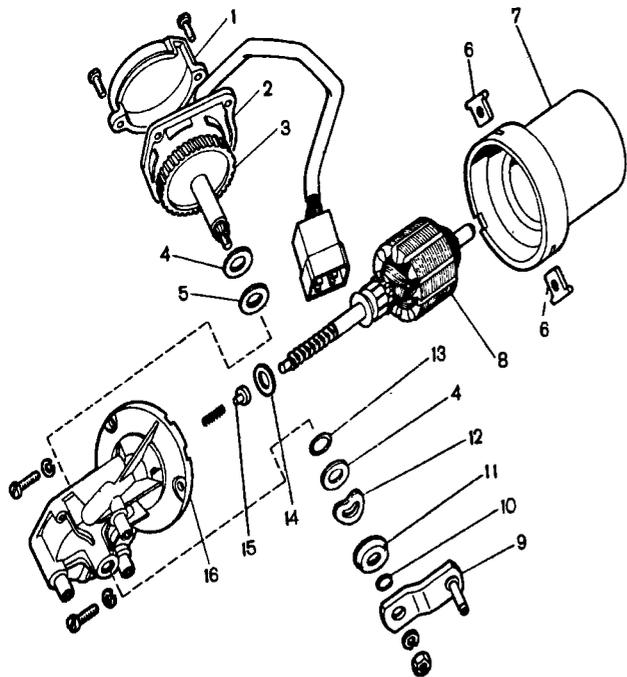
Детали электродвигателя стеклоочистителя: 1 - крышка; 2 - панель; 3 - шестерня редуктора; 4 - стальная шайба; 5 - текстолитовая шайба; 6 - сухарь; 7 - корпус; 8 - якорь; 9 - кривошип; 10 - стопорное кольцо; 11 - защитный колпачок; 12 - пружинная шайба; 13 - уплотнительное кольцо; 14 - регулировочная шайба; 15 - подпятник; 16 - крышка электродвигателя
